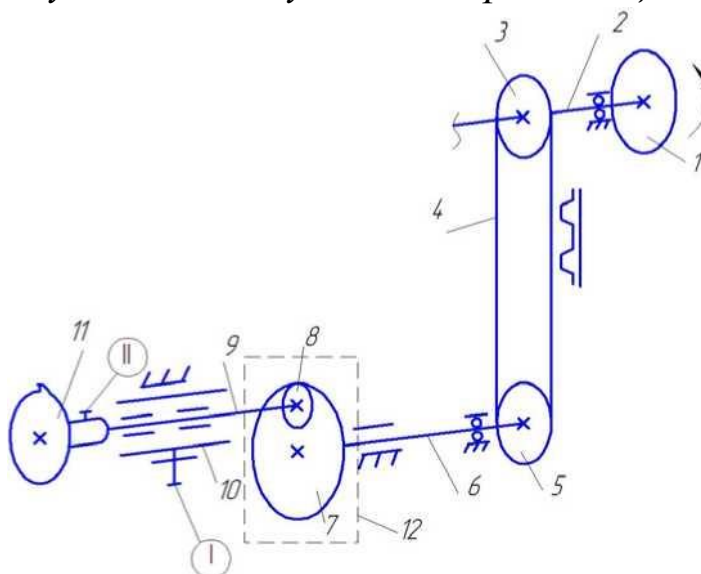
Пространственная структурная схема механизма челнока. 1 - шкив - маховик; 2 - главный вал; 3 - верхний зубчатый барабанчик; 4 - плоскозубчатый ремень; 5 - нижний зубчатый барабанчик; 6 - распределительный вал; 7 - цилиндрическое зубчатое колесо с внутренними зубьями; 8 - шестерня с внешними зубьями; 9 - челночный валик; 10 - корпус устройства автоматической смазки челнока; 11 - челнок; 12 - картер.
